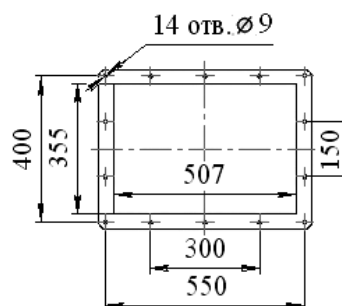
Вентиляторы ВПИ-PRU-630. Присоединительные размеры
